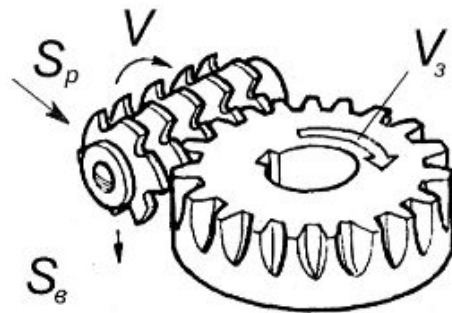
Нарезание зубьев цилиндрического колеса червячной фрезой
